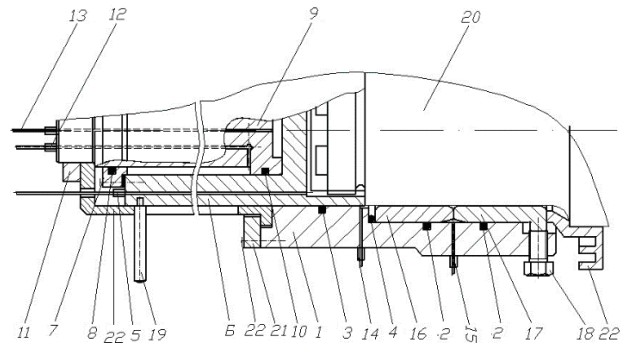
Устройство для распрессовки и запрессовки колец буксовых подшипников колёсных пар
